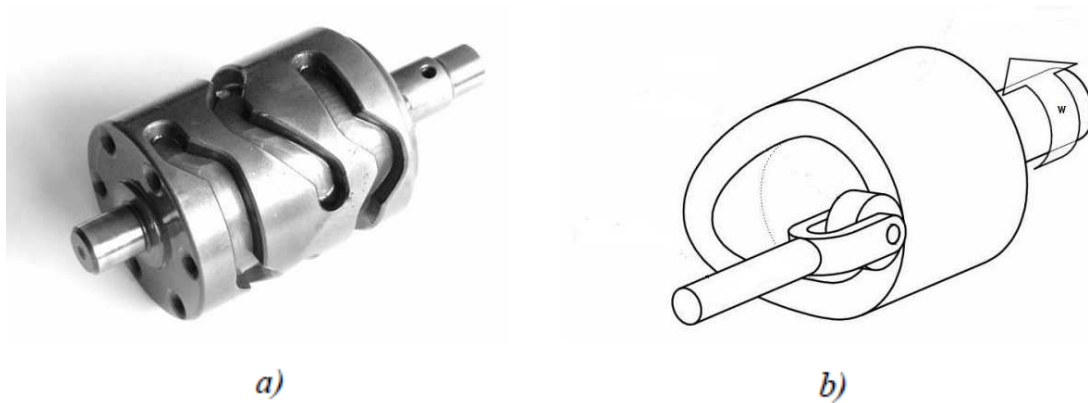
a) Leva axial de cara. b) Leva axial cilíndrica.
